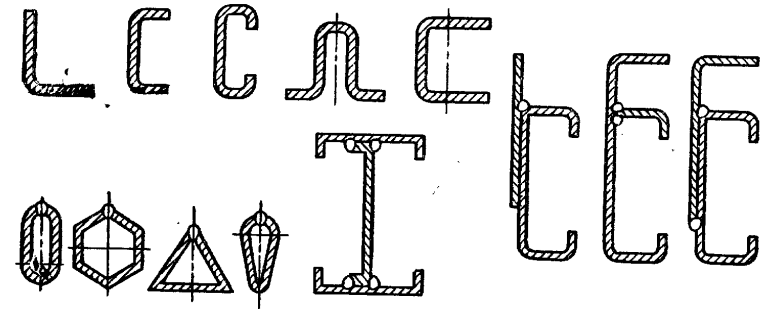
Конструкции балок из гнутых и штампованных элементов
